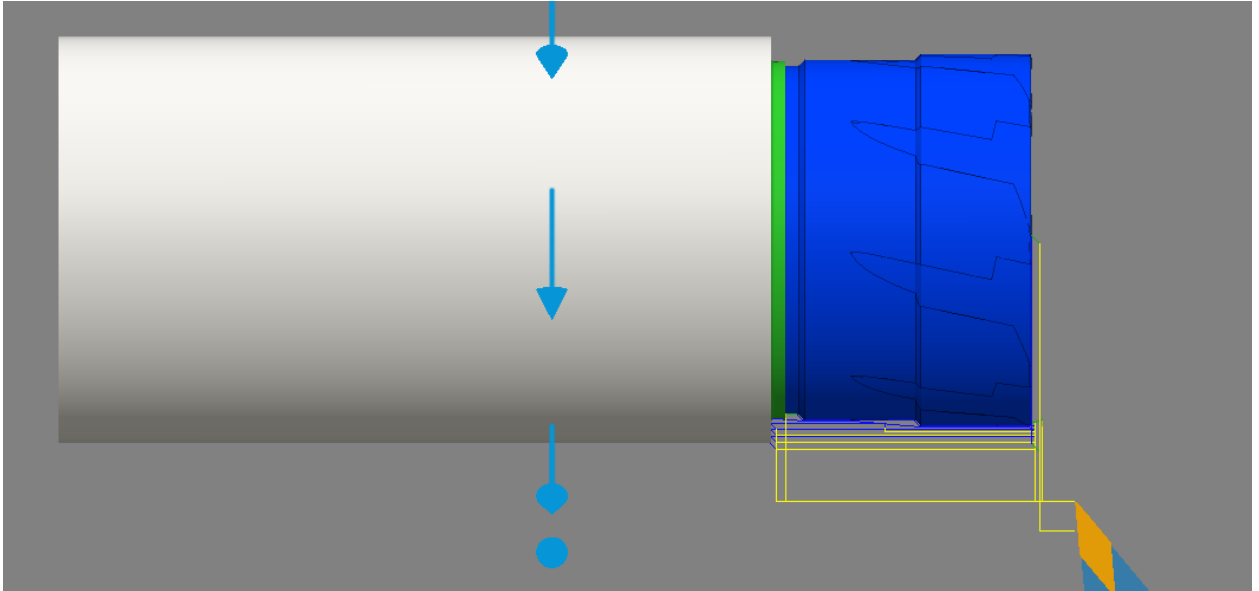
Торцювання, чорнова та чистова обробки
